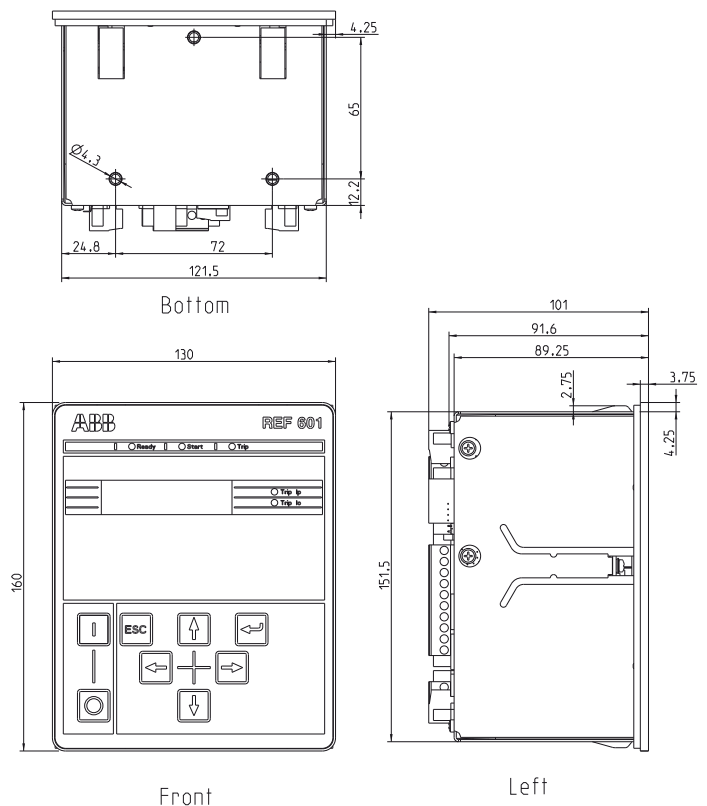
Dimensioni di montaggio del relè con montaggio a filo (pannello)
